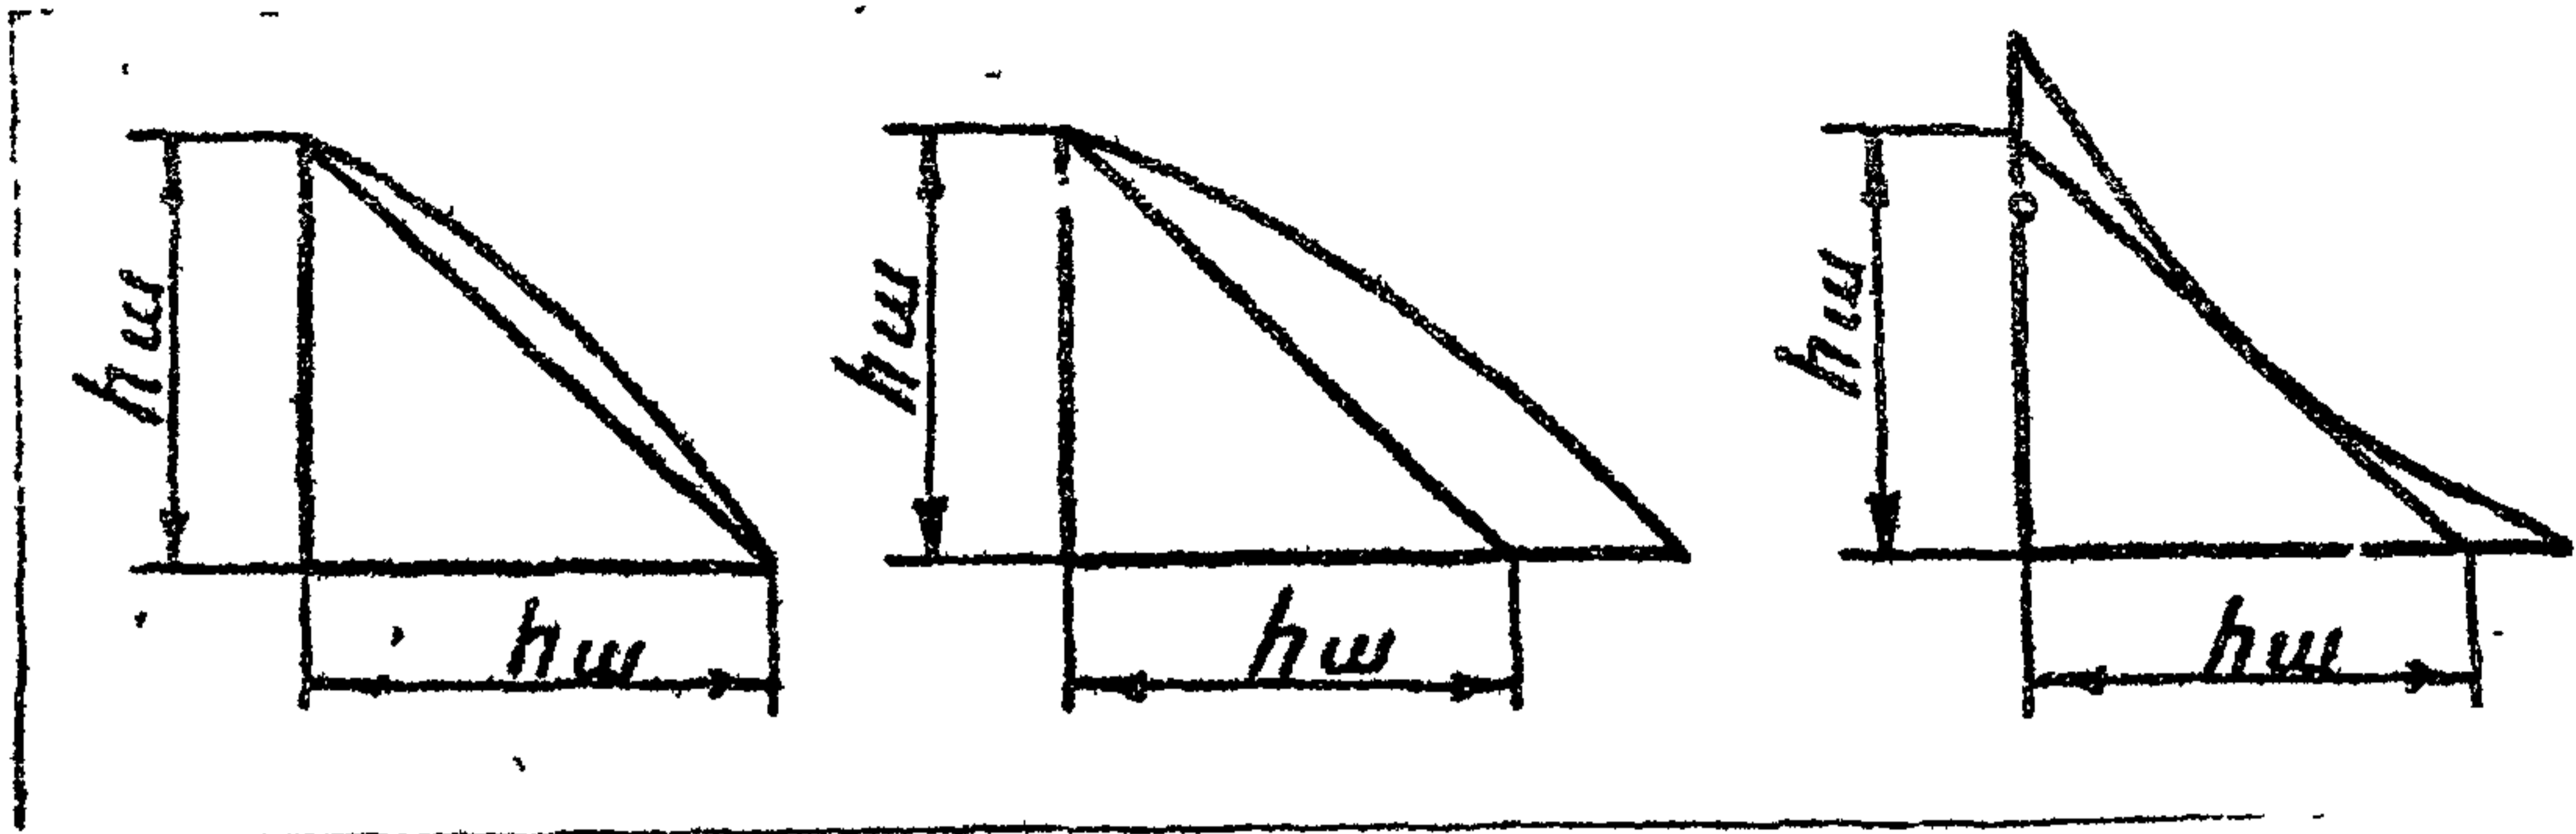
Схемы сечений сварных угловых швов
